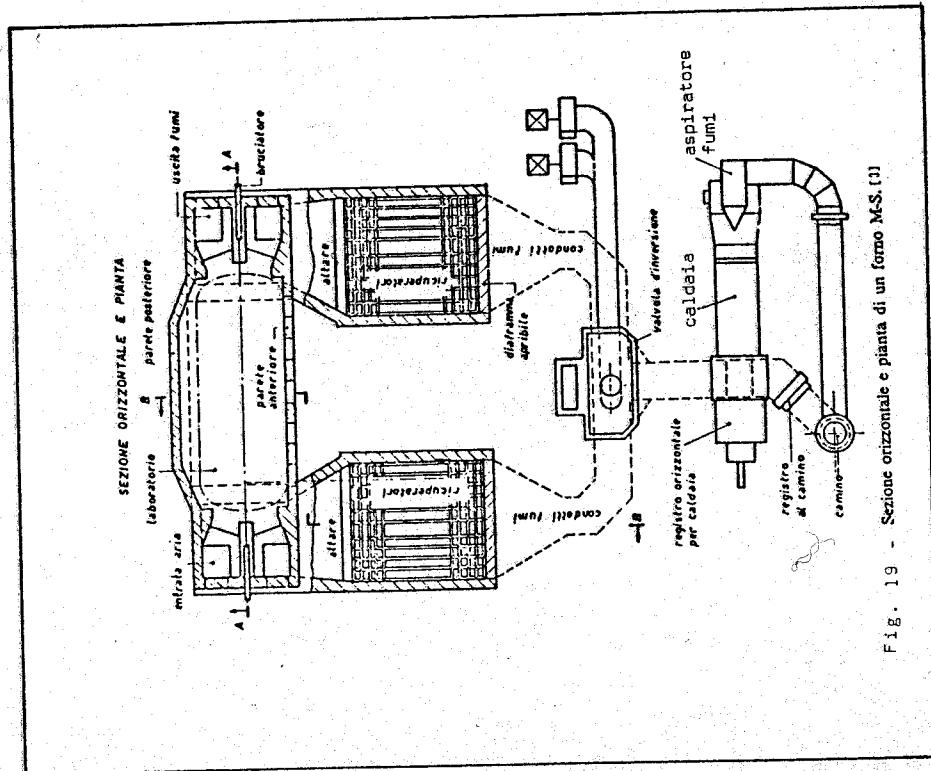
Sezione orizzontale e pianta di un forno M.S. [1]
